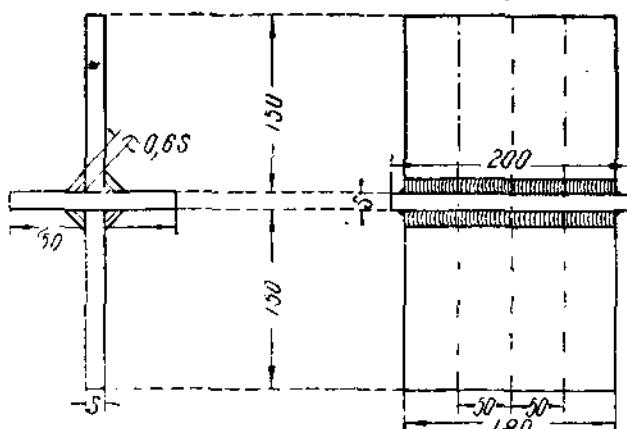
Образец для валиковой торцовой сварки (тип а).
